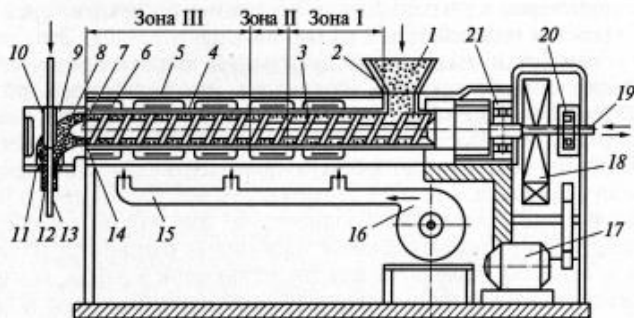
Схема одночервячного экструдера: 1- перерабатываемый полимер; 2 – загрузочная воронка экструдера; 3 – червяк; 4 – втулка; 5 – рабочий цилиндр; 6 – нагреватель; 7 – насадка червяка; 8 – расплав полимера; 9 – головка экструдера; 10 – дорн; 11 – матрица; 12 - экструдруемый слой; 13 – элемент конструкции, на который наносится слой полимера; 14 – решетка; 15 – внешнее охлаждение цилиндра; 16 – вентилятор; 17 – электродвигатель; 18 – редуктор; 19 – охлаждающая ванна; 20, 21 - подшипники
